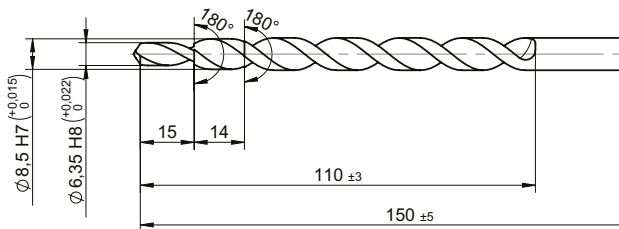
Stufenbohrer Typ 1337A für Montagenippel M10x1
